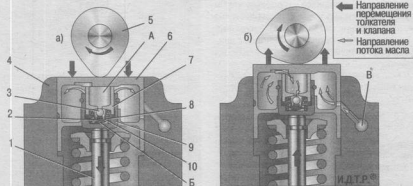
Схема работы гидротолкателя в клапанном механизме двигателя ВАЗ-11194: 1 — клапан; 2 — пружина обратного клапана; 3 — обратный клапан; 4 — головка блока цилиндров; 5 — кулачок распределительного вала; 6 — толкатель; 7 — плунжер; 8 — пружина плунжера; 9 — гильза; 10 — корпус обратного клапана; А, Б — полости гидротолкателя; В — масляный канал
